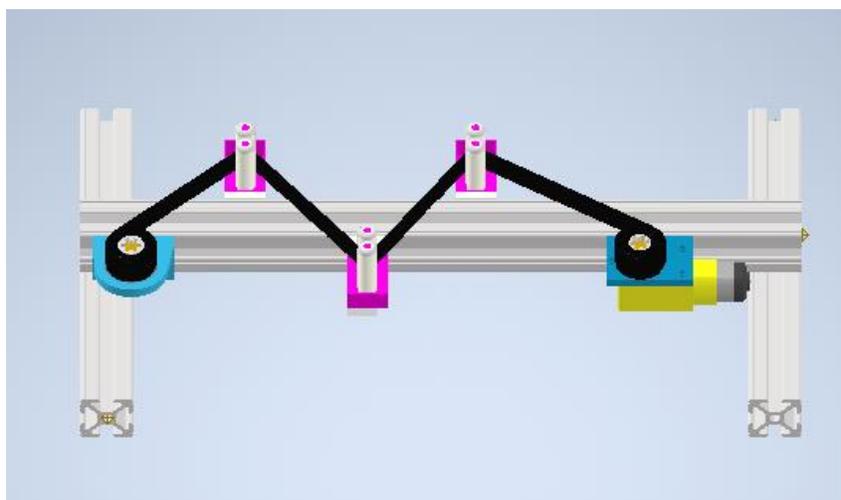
Ensamble de todas las piezas del dispositivo (vista superior).
